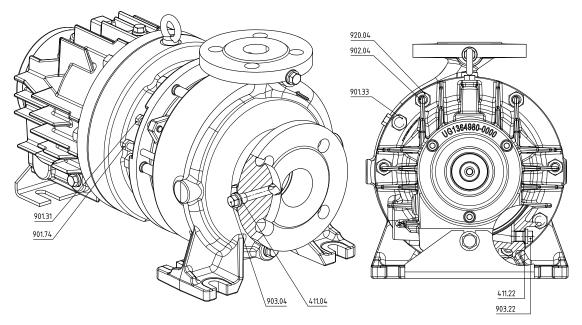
Крепление крышки с напорной стороны на корпусе насоса для исполнения с зажимной крышкой
